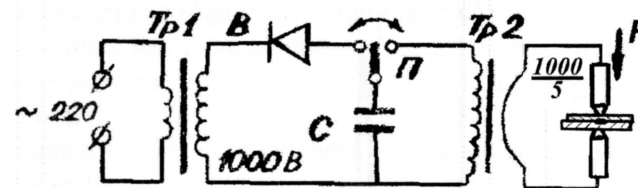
Схема конденсаторной трансформаторной сварки
